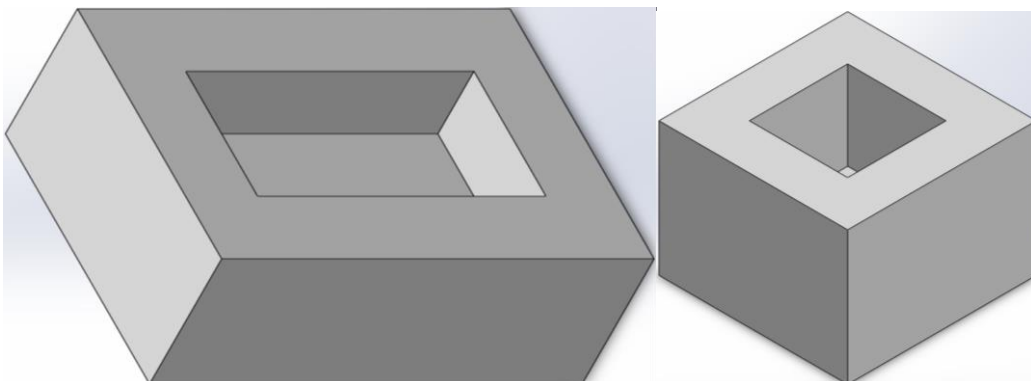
Mitad del aislante con corte vertical y con corte horizontal
